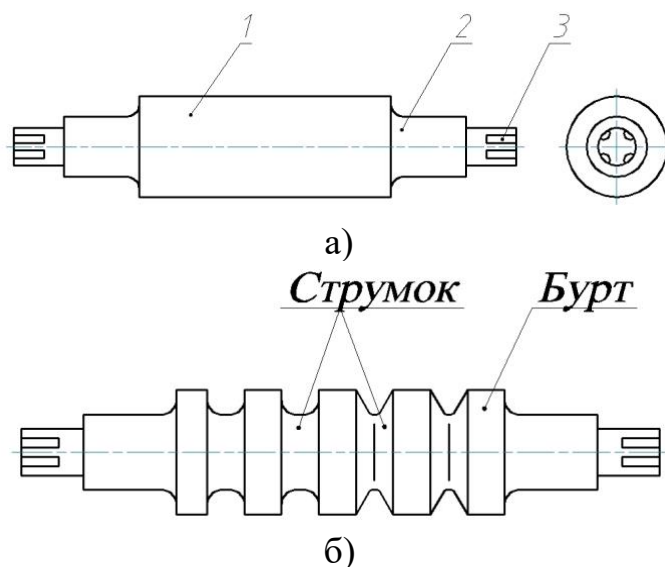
Прокатні валки: а) – гладкий; б) – калібрований.
